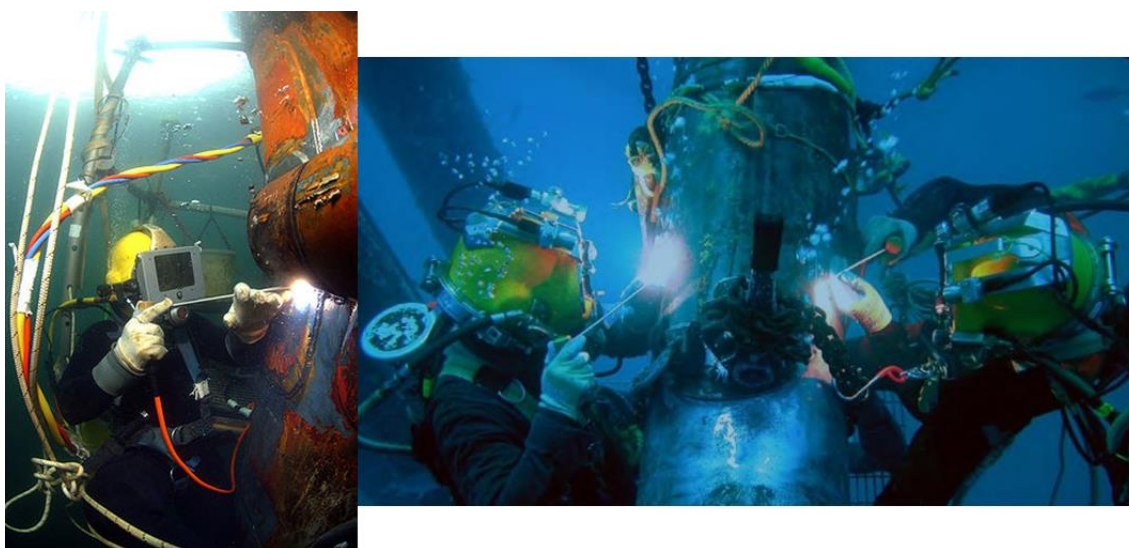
2 - Soldagem Subaquática Molhada [2].
